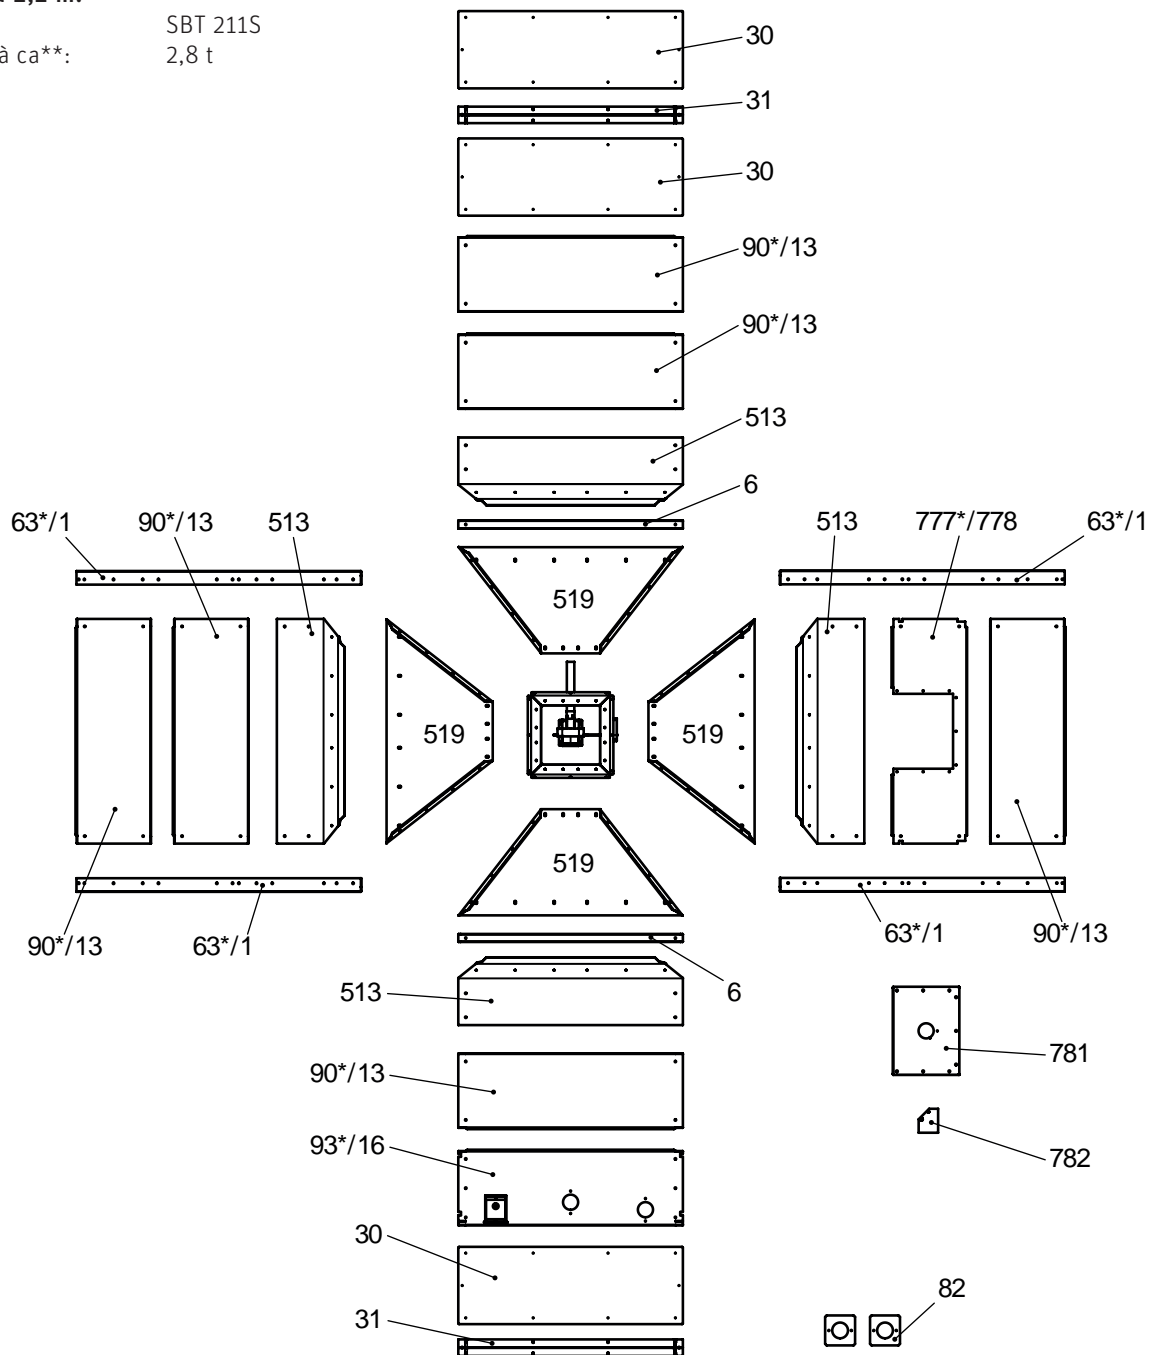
Singoli pezzi del serbatoio in lamiera d'acciaio – vista dall'alto
